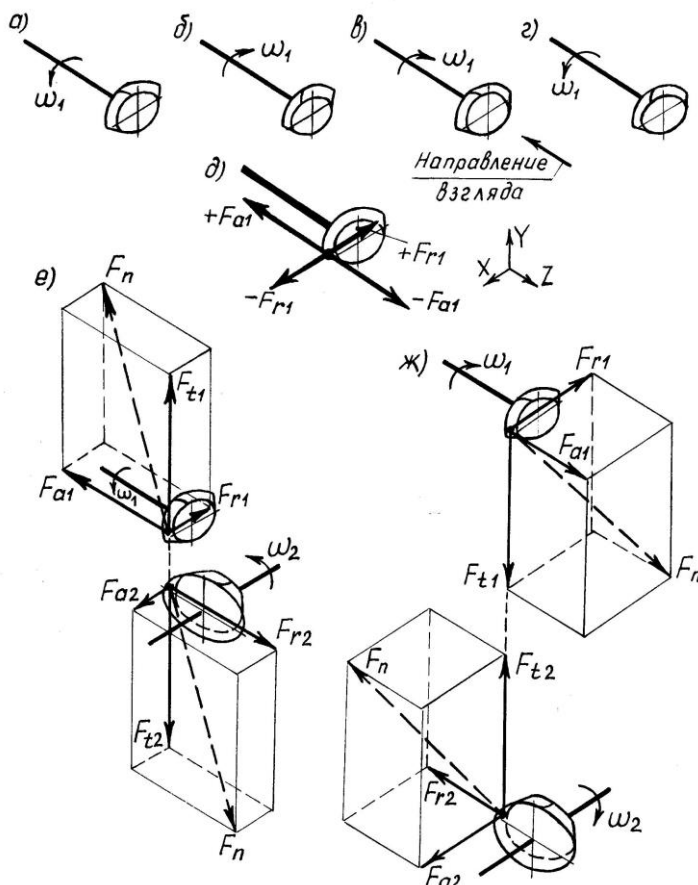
Силы в зацеплении конической зубчатой передачи с круговыми зубьями
